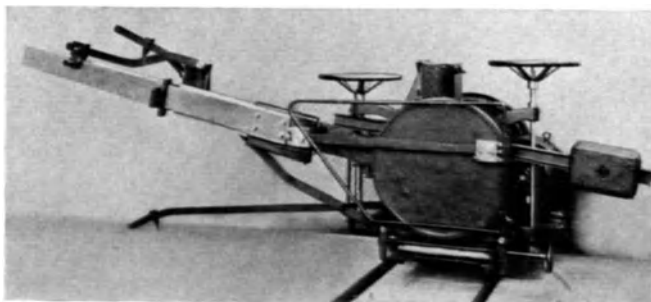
Maschinell angetriebener Fuchsschwanz.
